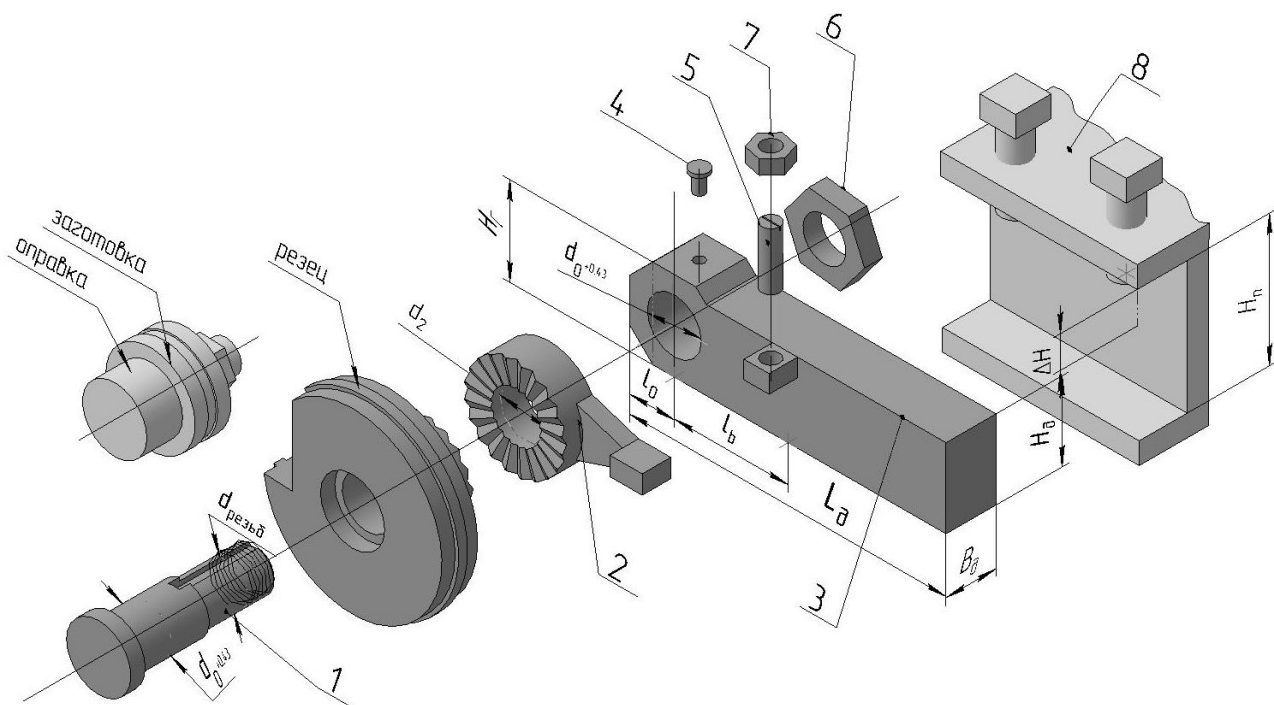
Схема установки круглого фасонного резца на державке I типа. Конструктивные параметры корпуса державки:
